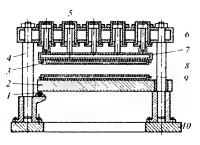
Балочный пресс для скленки широких полировальных лент: I — роликовые упоры, 2 — нижияя траверса; 3 — верхняя прессующая планка; 4 — ко-
